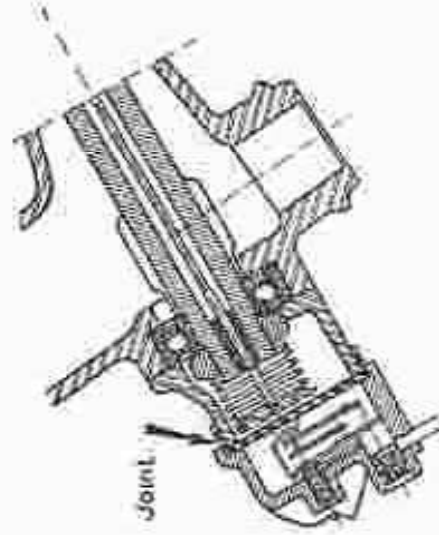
Vue en coupe du boîtier de carter et du boîtier de direction.
